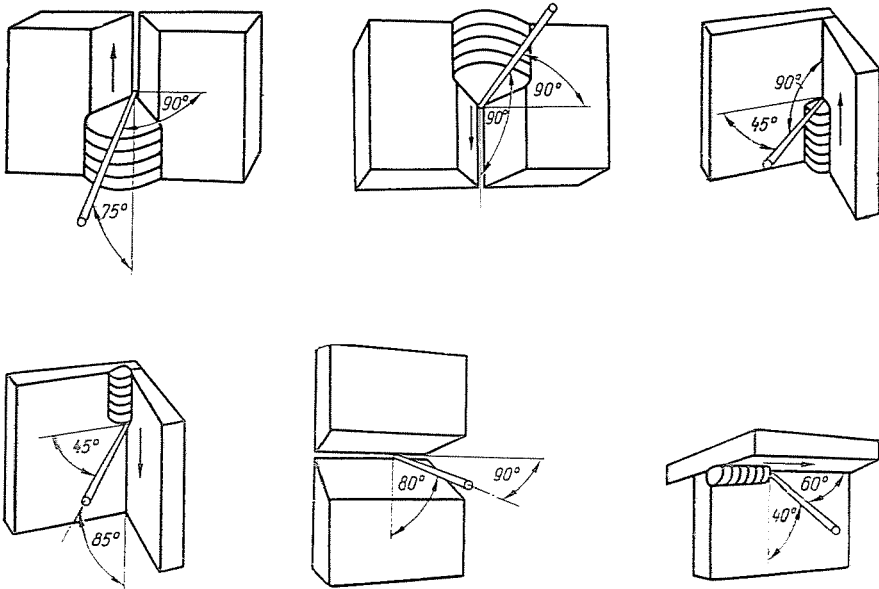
Richtige Haltung des Brenners in verschiedenen Schweißpositionen
